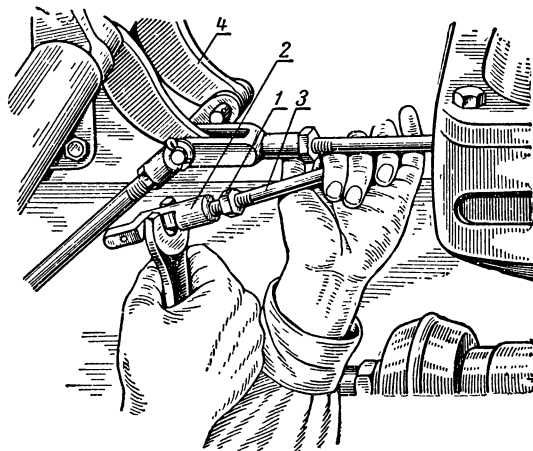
Регулировка тяги механизма блокировки на тракторе ДТ-54А:
